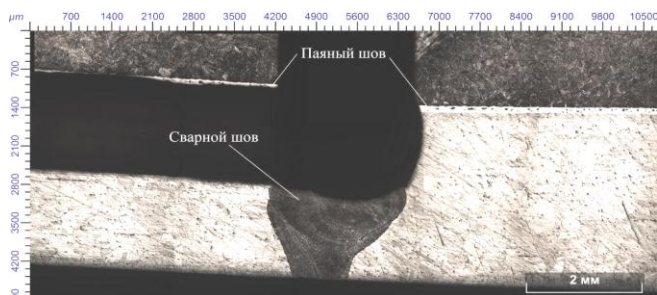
Фото сварного шва паяной оболочки при “новом” режиме
